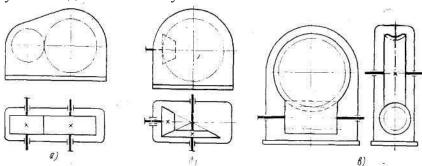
Схемы редукторов: а — одноступенчатый с цилиндрическими колесами, б — одноступенчатый с коническими колесами, в— одноступенчатый червячный
